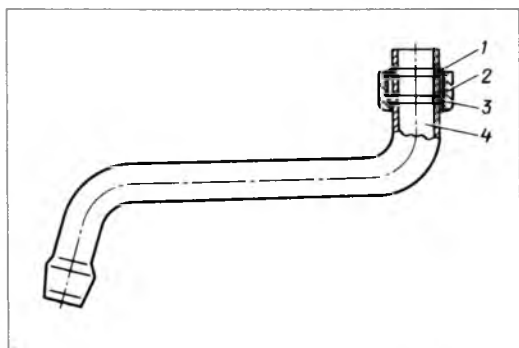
Излив современной конструкции: 1 — резиновое кольцо; 2 — накладная гайка; 3 — разжимное пластмассовое кольцо; 4 — трубка
